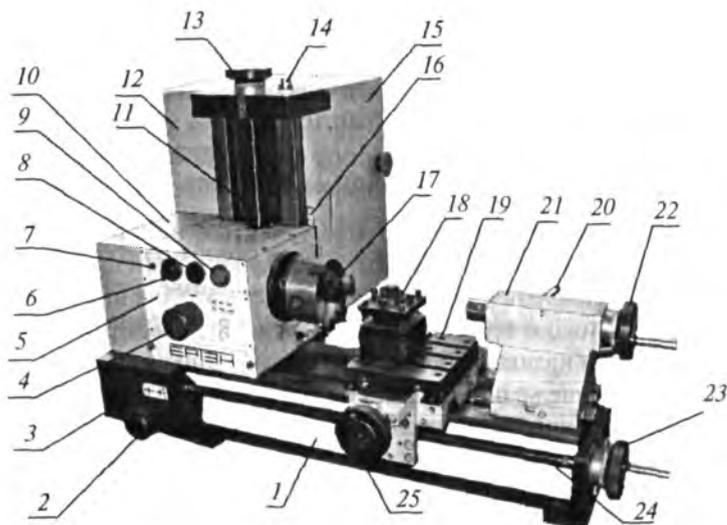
Малогабаритный широкоуниверсальный станок мод. ЕРТОЗ (ЕРТОЗ-1)
